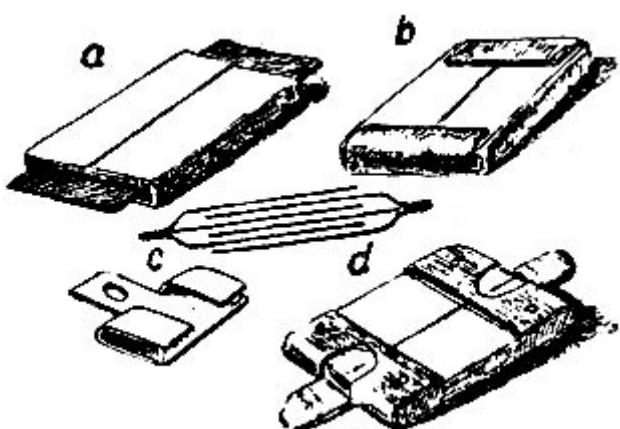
Изготовление блокировочного конденсатора, а – собранные листики фольги и бумаги; ниже вид взаимного расположения листиков фольги; б – концы листиков фольги загнуты наружу; в – обойма из листовой латуни для зажимания концов фольги; д – готовый конденсатор
